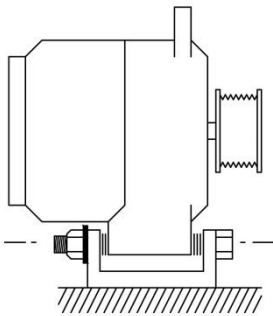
Montaggio dell'alternatore - montaggio su piedino
